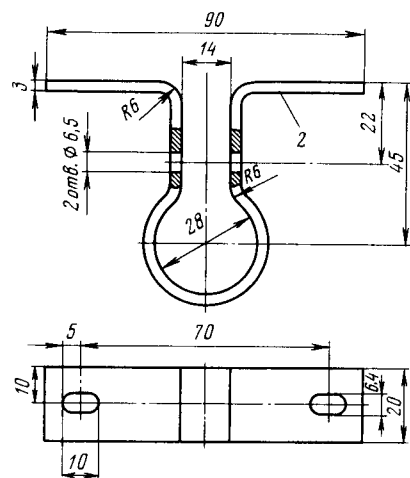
Детали для установки полупрозрачного наполнителя бачка главного тормозного цилиндра:
